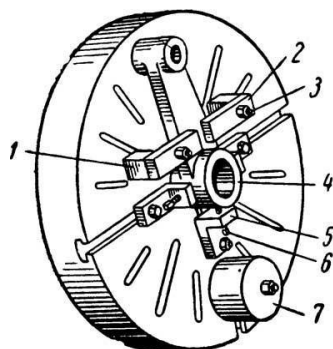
Планшайба (1 – підставка прихвату, 2 – прихват, 3 – гвинт прихвата, 4 – деталь, 5 – направляючий кутник, 6 – гвинт регулювання, 7 – балансир)
